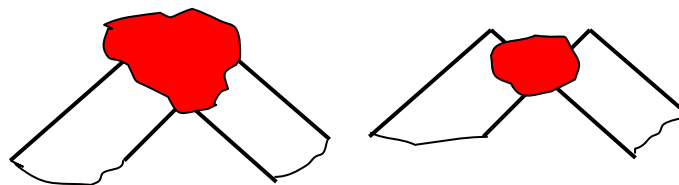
Defectos comunes en la soldadura de juntas de esquina en posición plana , con aporte .
